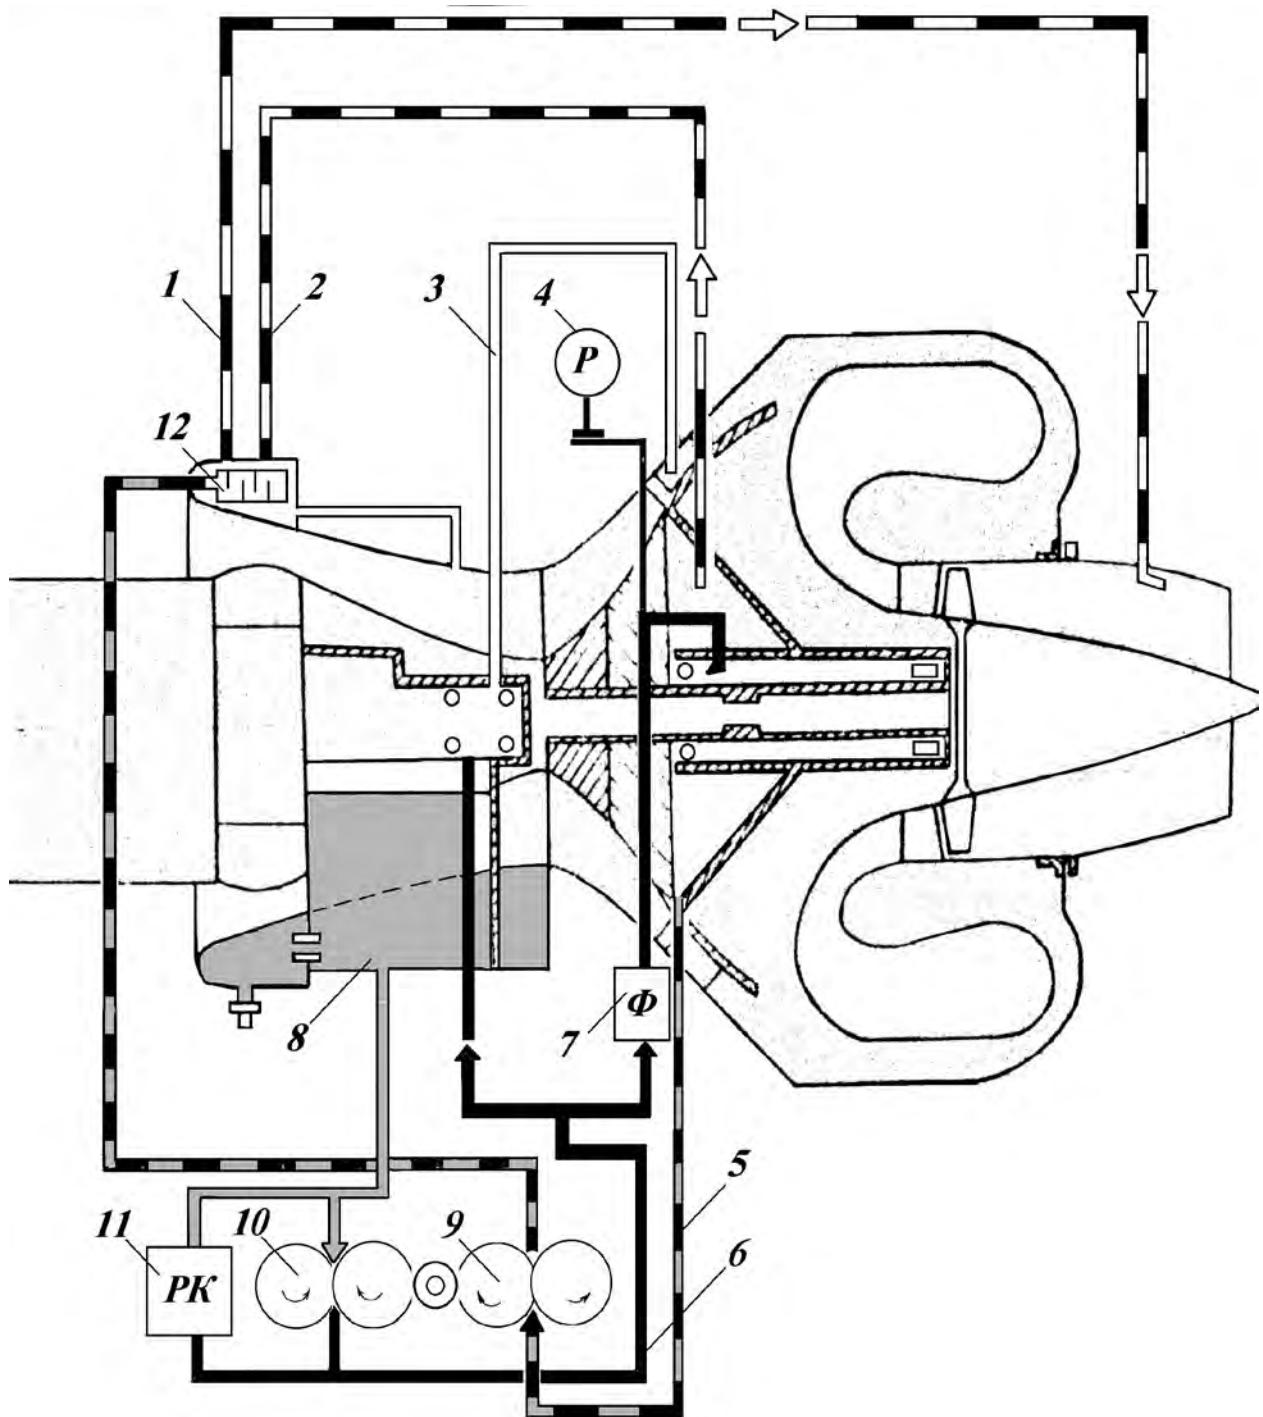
9. Система смазки и суфлирования двигателя АИ-9В:
